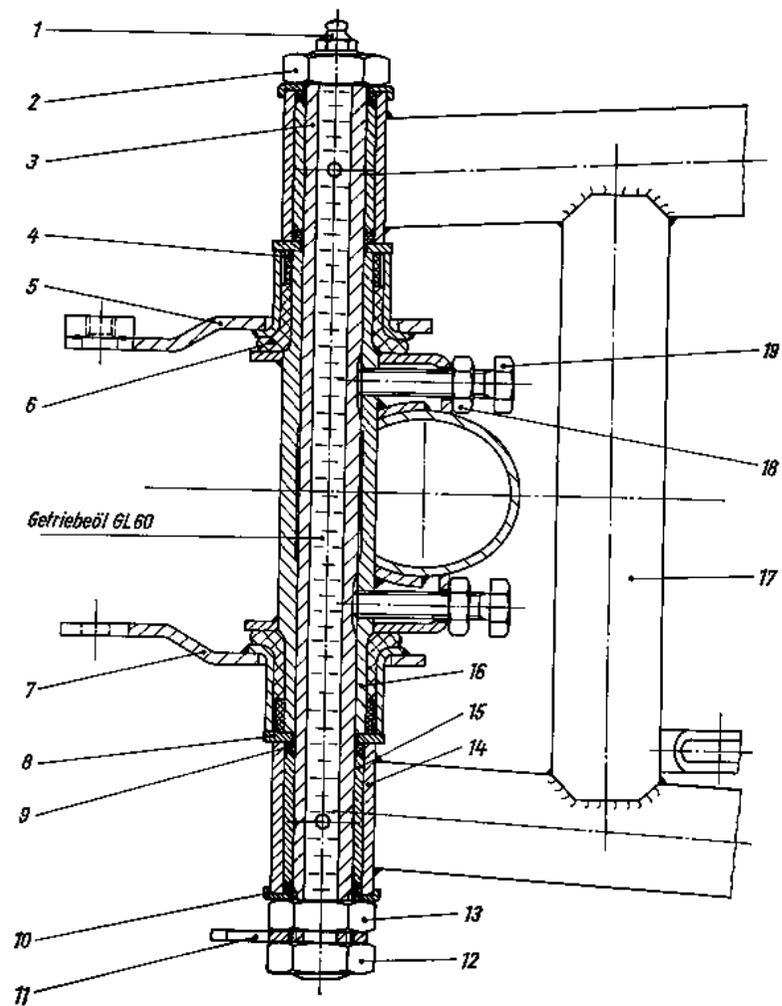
Schwingenlagerung und elastische Lagerung der hinteren Motorbefestigungsbleche (Schnittzeichnung)
